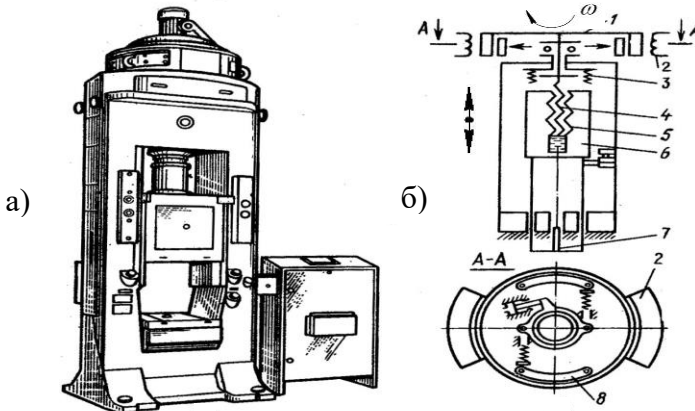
Схема гвинтового преса з дугостаторним приводом: а) загальний вигляд; б) кінематична схема;
